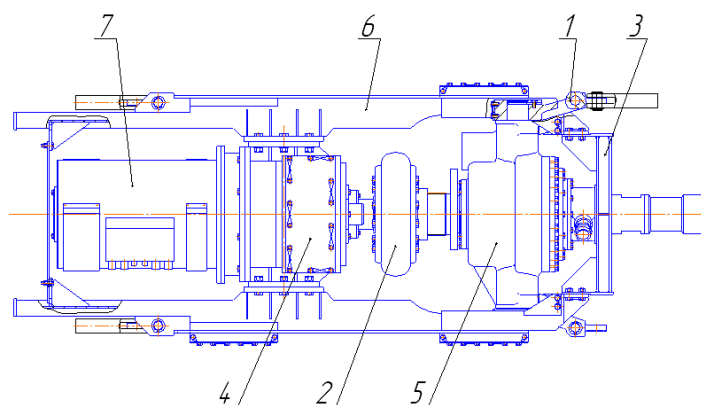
Головка бурового снаряда: 1 - ползун; 2 - муфта шинно-зубчатая; 3 - траверса; 4 - редуктор вращателя; 5 - узел опорный; 6 - каретка; 7 - электродвигатель
